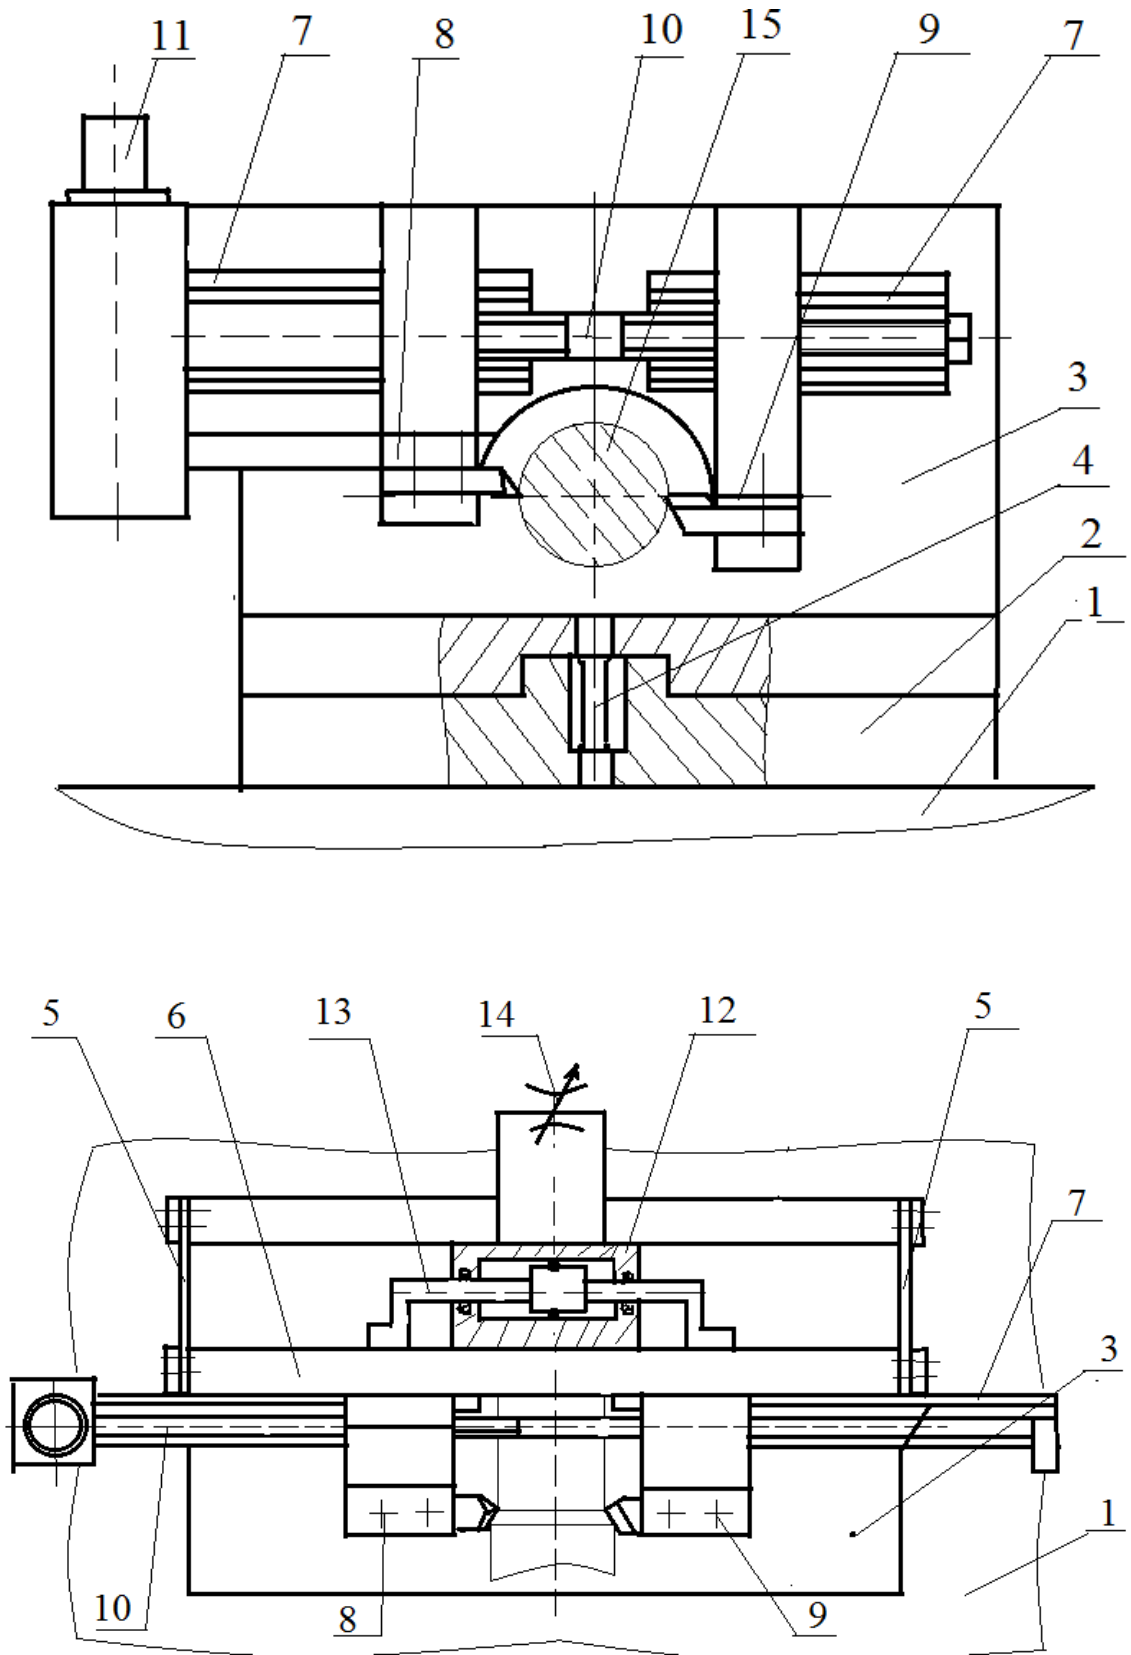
Загальний вигляд дворіцевої установки для обробки валів із пристроєм вирівнювання
